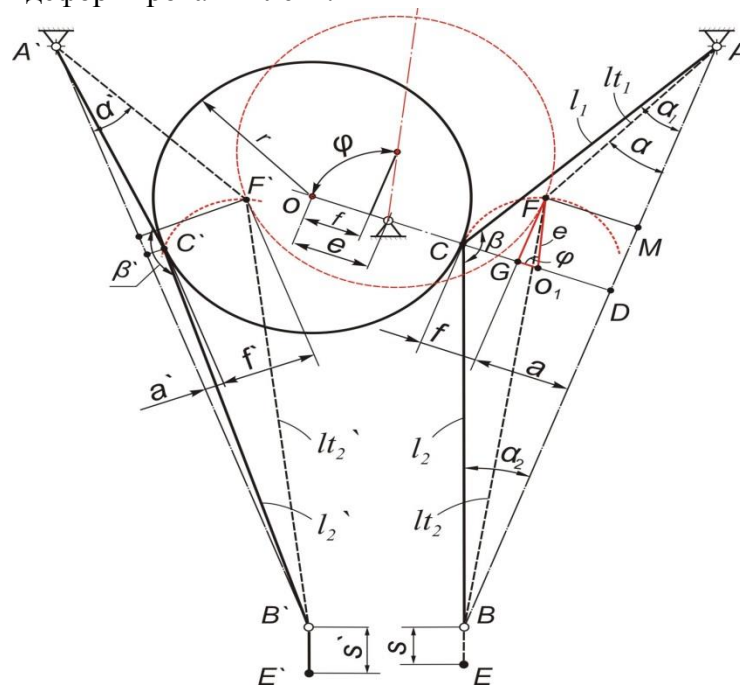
Кинематическая схема устройства для наплавки двумя ленточными электродами
